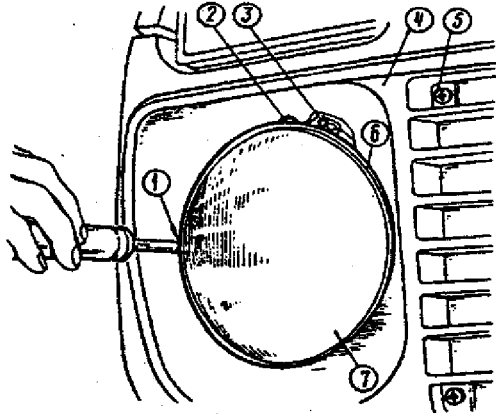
Conjunto do farol: 1 - parafuso de ajuste horizontal; 2 - parafuso de ajuste vertical; 3 - parafuso de fixação do aro do farol; 4 - conjunto da grade dianteira e moldura dos faróis; 5 - parafuso de fixação da moldura; 6 - aro do farol; 7 - elemento ótico.
